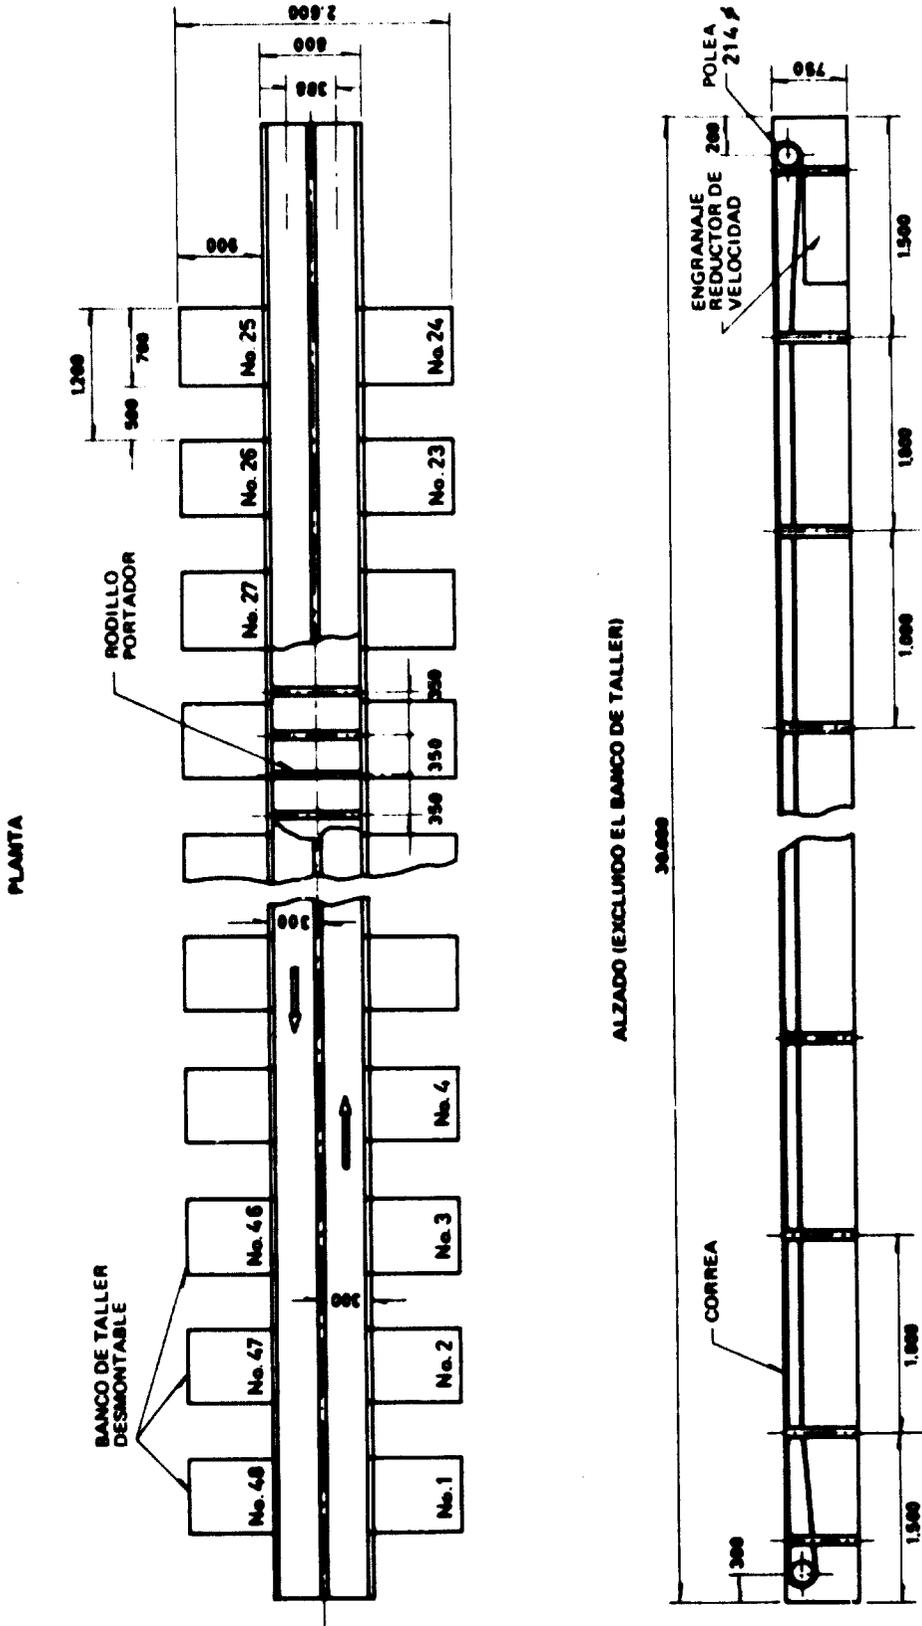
Planta (vista superior) y alzado (vista posterior) de un sistema típico de doble correa transportadora (dimensiones en mm)
